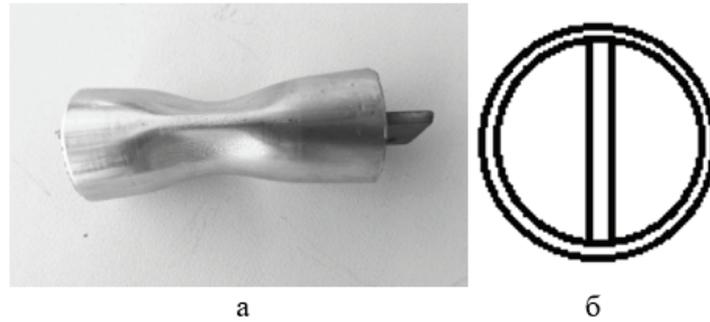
А — сборочный вид заготовки и распорки; б — эскиз расположения распорки в заготовке
